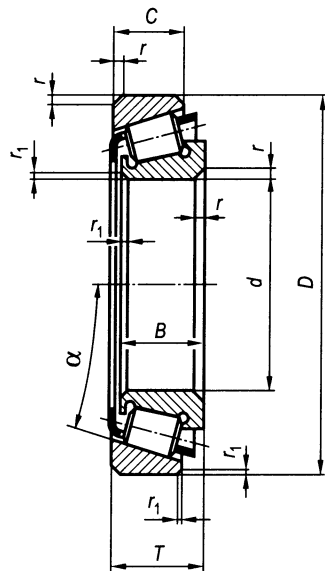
Подшипник роликовый радиально-упорный конический однорядный
